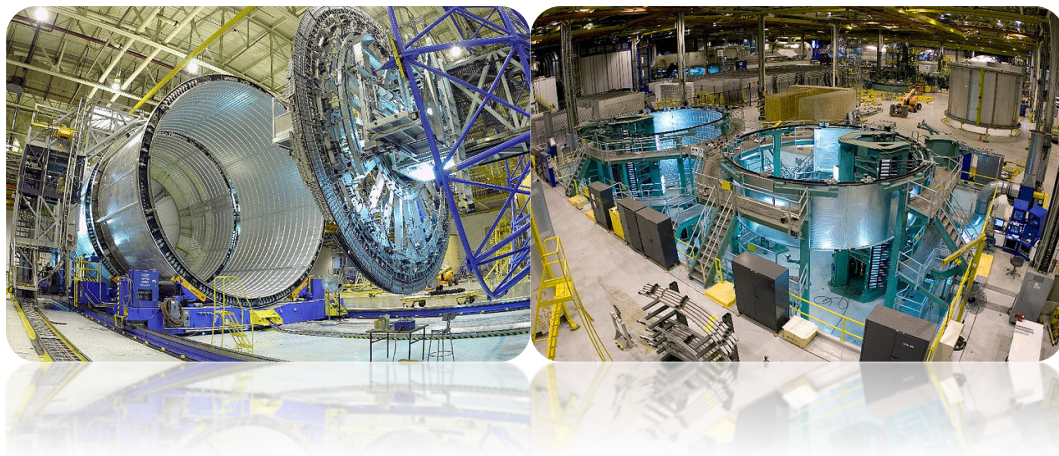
Zona de treball de soldadura del 'Space Shuttle'.
